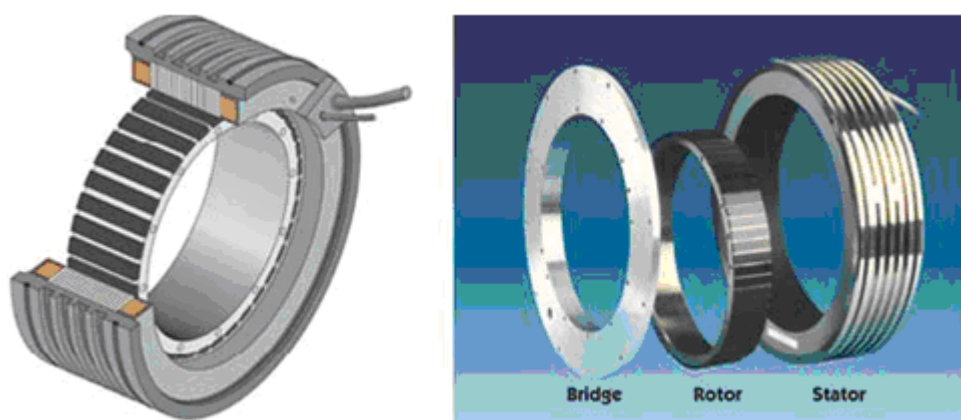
Elementos de um Direct Drive fabricados pela Toyo Denky Seizo
